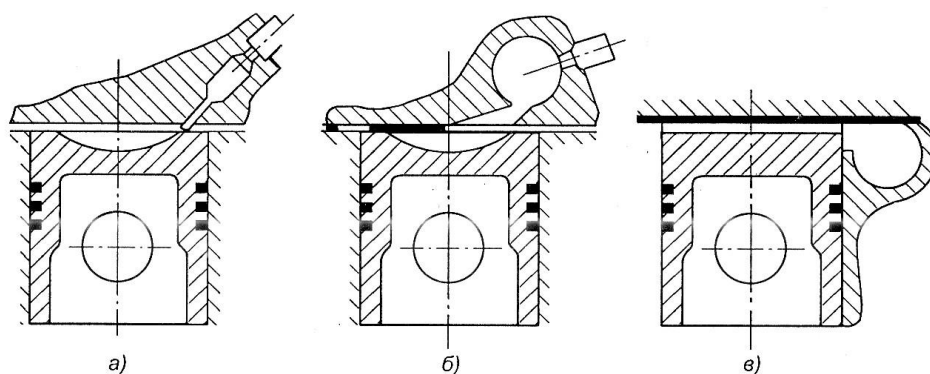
Камеры сгорания дизелей разделенного типа: а – предкамера; б – вихревая камера в головке блока; в – вихревая камера в блоке
